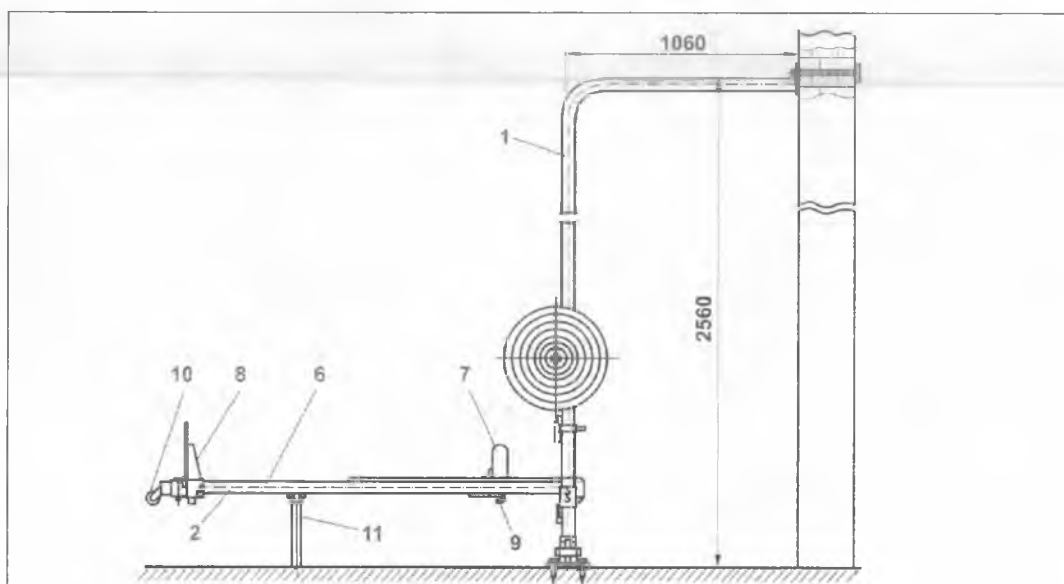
Универсальная установка для тренировки тяжелоатлетов, крепящаяся на стене
